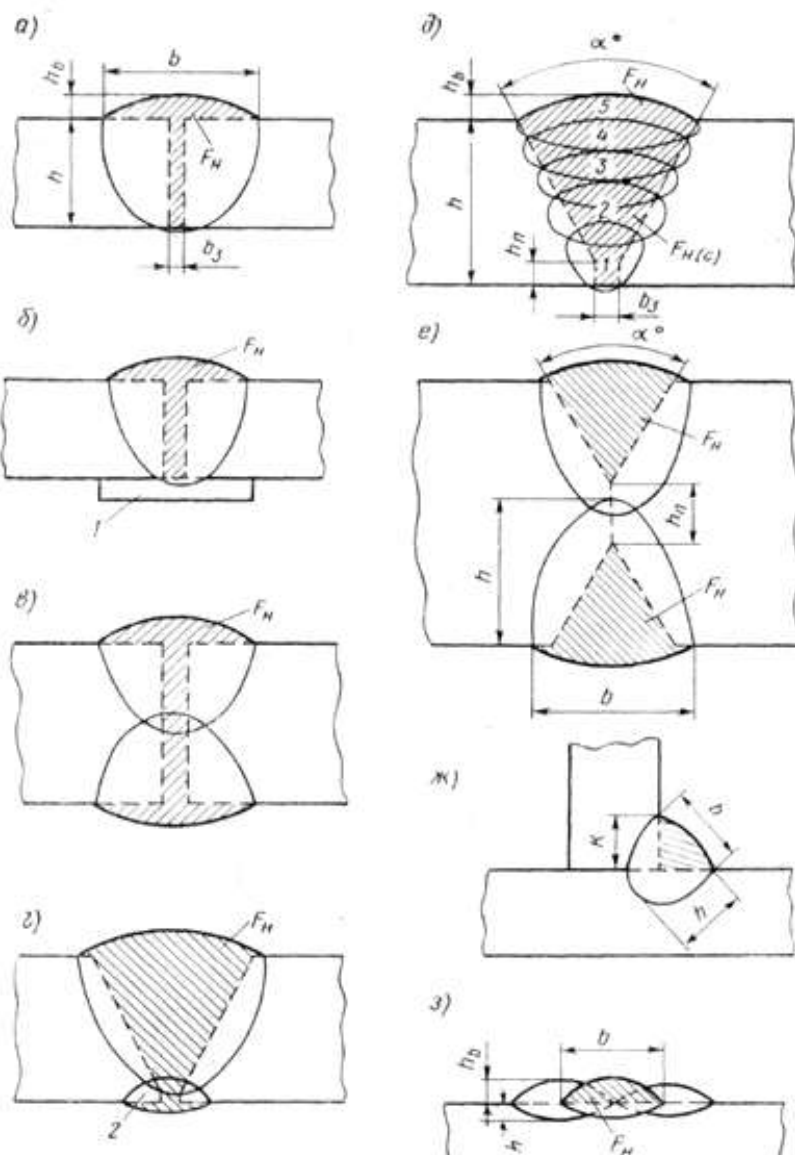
Размеры и форма подготовки кромок и сварного шва: а – 1-об-разный (без скоса кромок) односторонний стыковой шов; б – то же, с металлической (остающейся) подкладкой (1); в — 1-образный (без скоса кромок) двухсторонний стыковой шов; г – К-образный стыковой шов с подваркой (2) корня шва; д – V-образный многопроходный стыковой шов (цифры указывают номер прохода—слоя); е – X-образный двухсторонний стыковой шов; ж — угловой шов (без скоса кромки вертикального элемента); з – расположение валков при наплавке (наплавленный металл заштрихован, пунктиром показана первоначальная разделка кромок соединяемых элементов)
